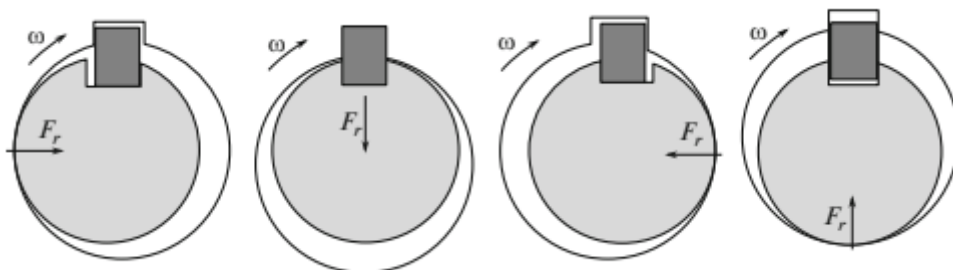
Поверхневий контакт під час обертання шарніру вал-втулка
